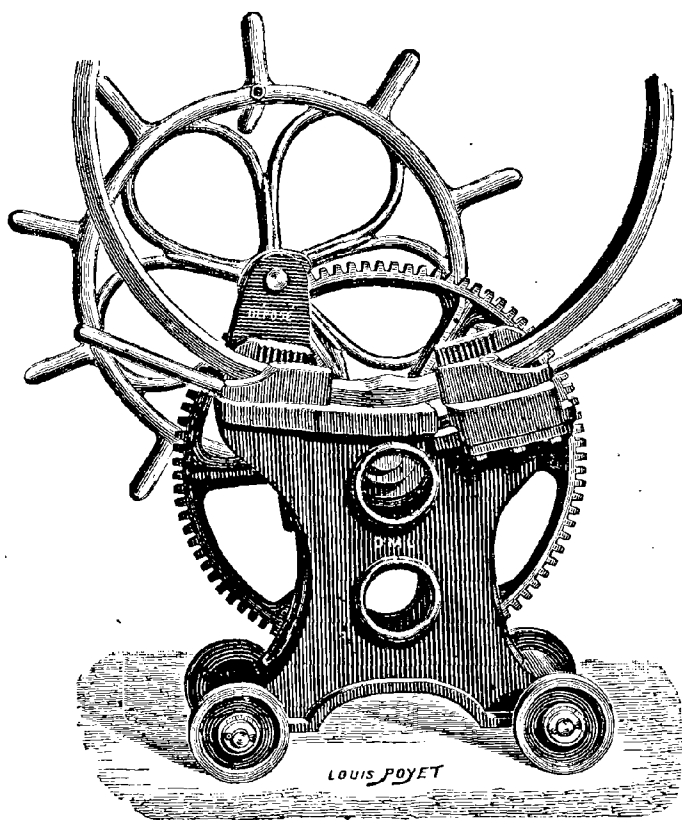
Machine à refouler et à souder. Dandoy-Mailliard.
